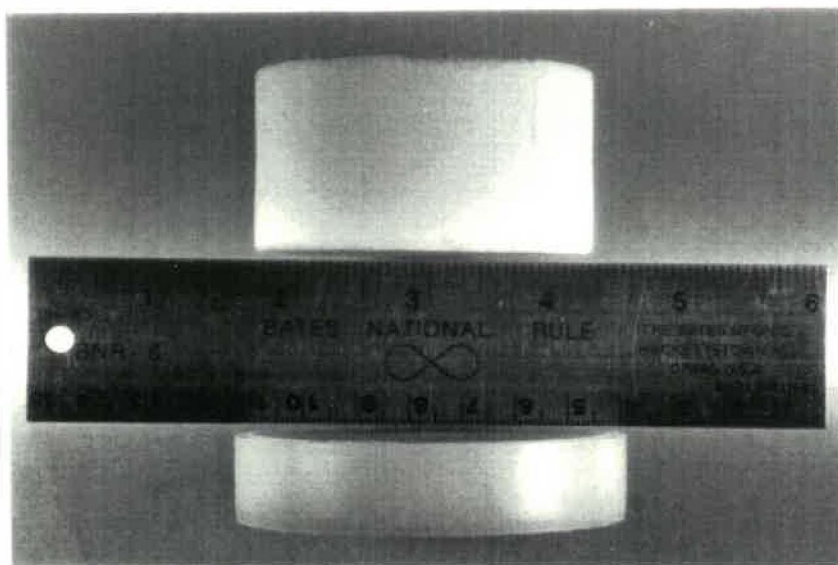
Dimension de la pré-forme et de la pièce moulée
